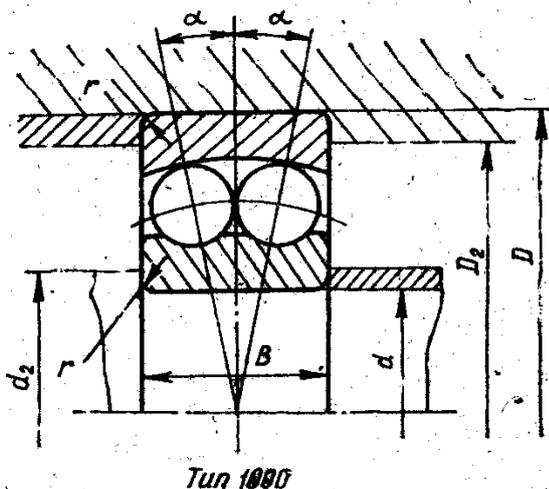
Шариковый самоустанавливающийся сферический двухрядный подшипник
